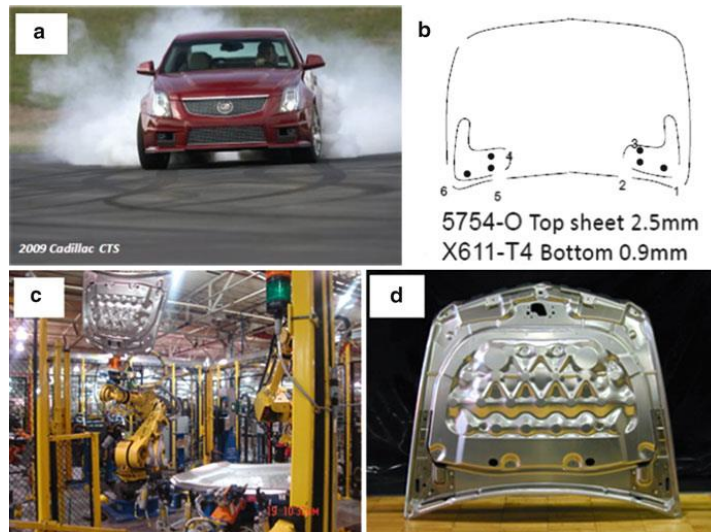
Ejemplos de la soldadura FSW en la industria del automóvil
